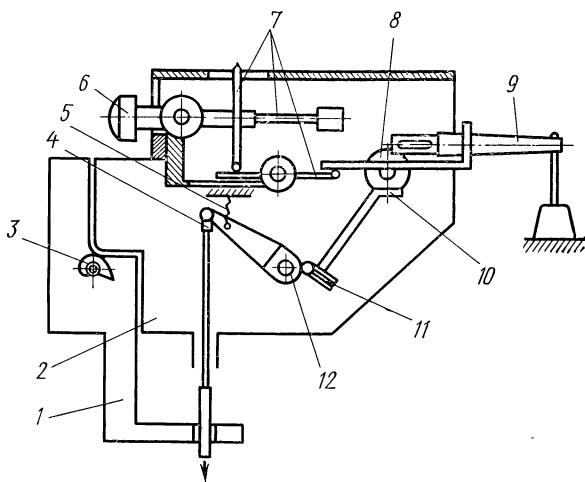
Конструктивная схема сварочной головки установки МС-41П2-1
